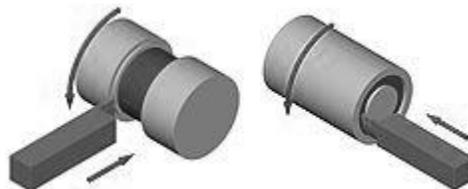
Ángulo de posicionamiento de la herramienta
